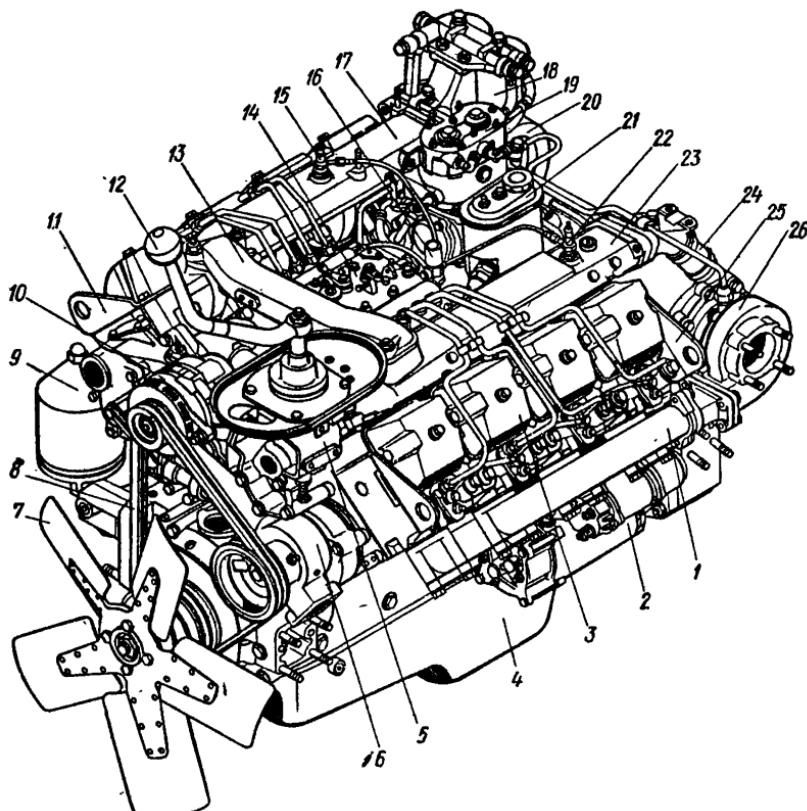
Двигатель КамАЗ-7403 с турбонаддувом:
